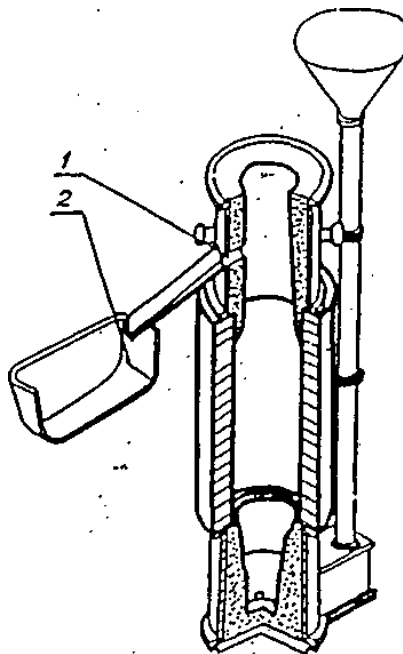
Стаціонарна кокільно-піщана форма для лиття валків методом «промивання» 1 — отвір у надливній частині валка, 2 - прийомний пристрій для зливу чавуну
